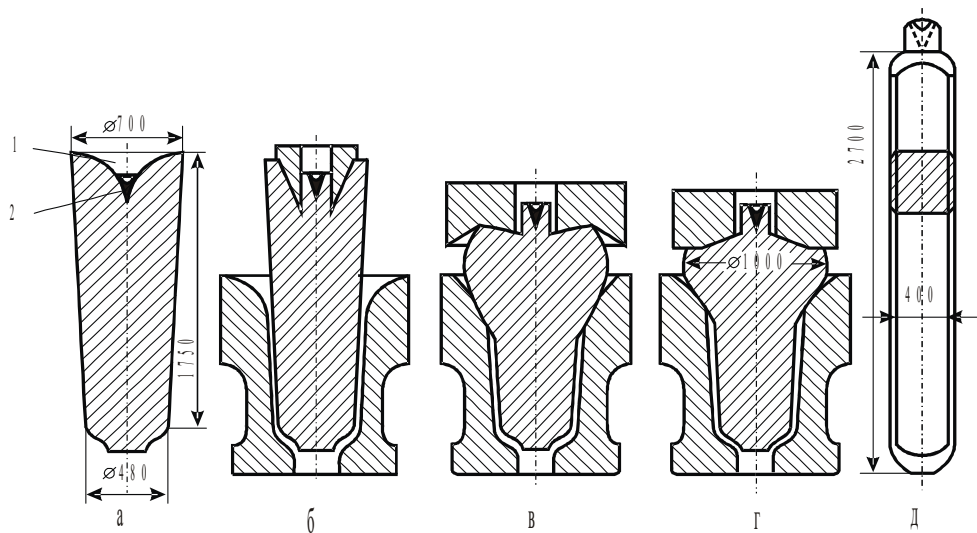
Схема видалення дефектної зони злитку: а – злиток; б – прошивка конусним полим прошивнем; в – висадка кільцевої зони злитку кільцем з виступом; г – висадка кільцем; д – протягнута заготовка; 1 – усадочна раковина; 2 – ліквацийна зона
